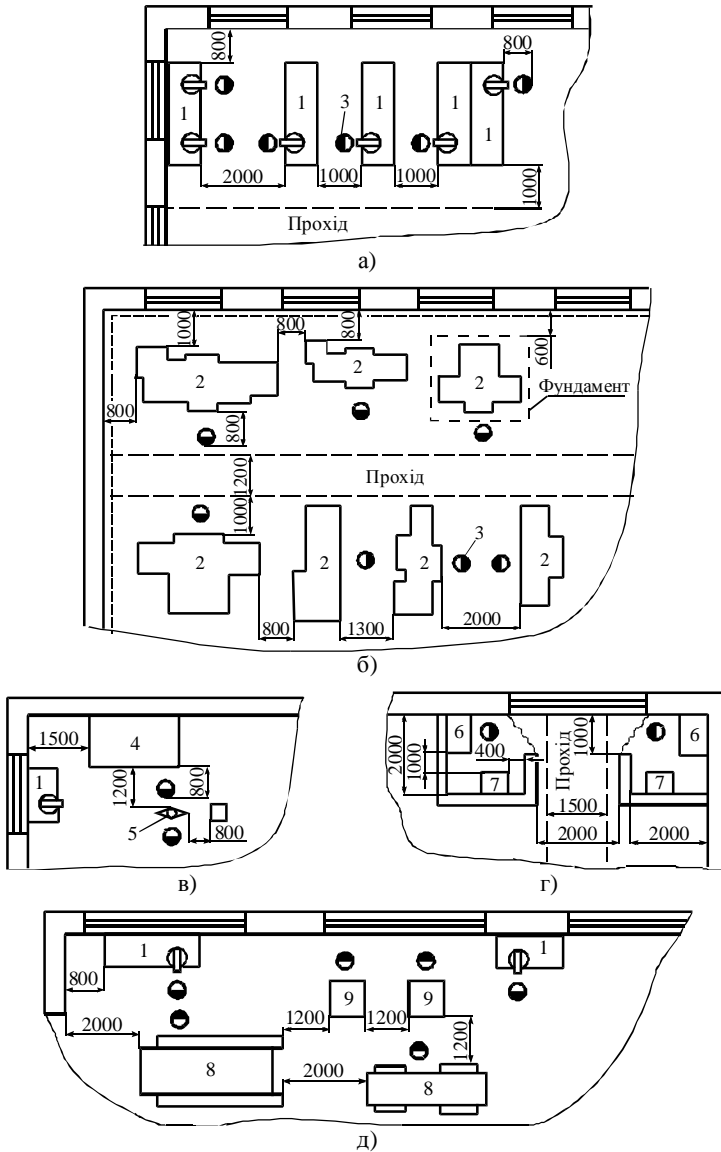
Орієнтовне компонування типових робочих місць слюсарного (а), механічного (б), ковальського (в), зварювального (г) відділень і ремонту тракторів (д): 1 – слюсарний верстак; 2 – верстат; 3 – робоче місце; 4 – горно; 5 – ковадло; 6 – зварювальний трансформатор; 7 – зварювальний стіл; 8 – трактор; 9 – агрегат
